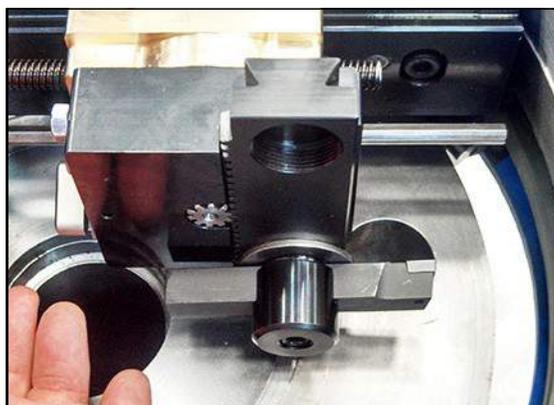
INSTALLER L'OUTIL HORIZONTALEMENT (FF1200 ILLUSTRÉE)
